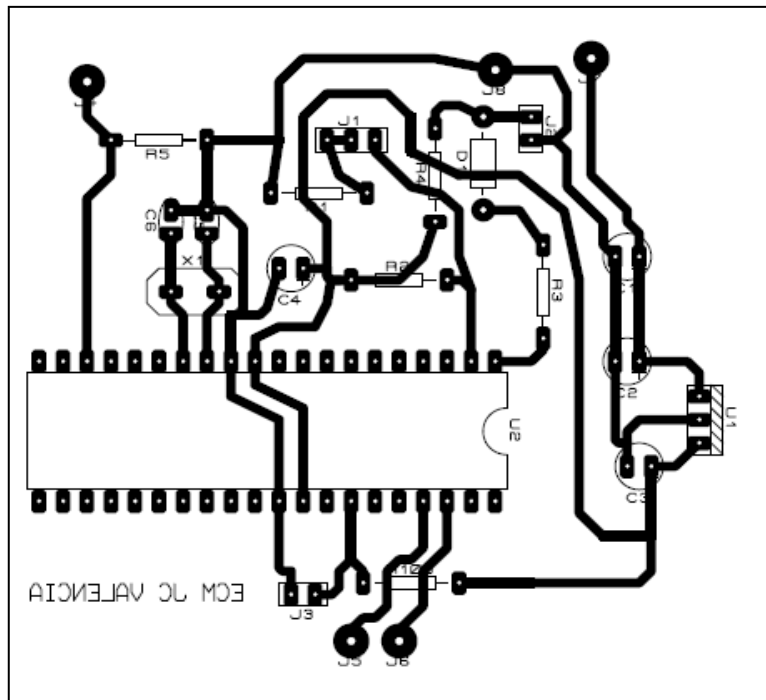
Diseño de la placa electrónica con sus componentes del ECM.
